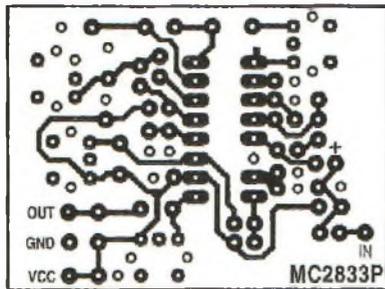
Reproduction à l'échelle 1 du circuit imprimé vu côté soudures.
